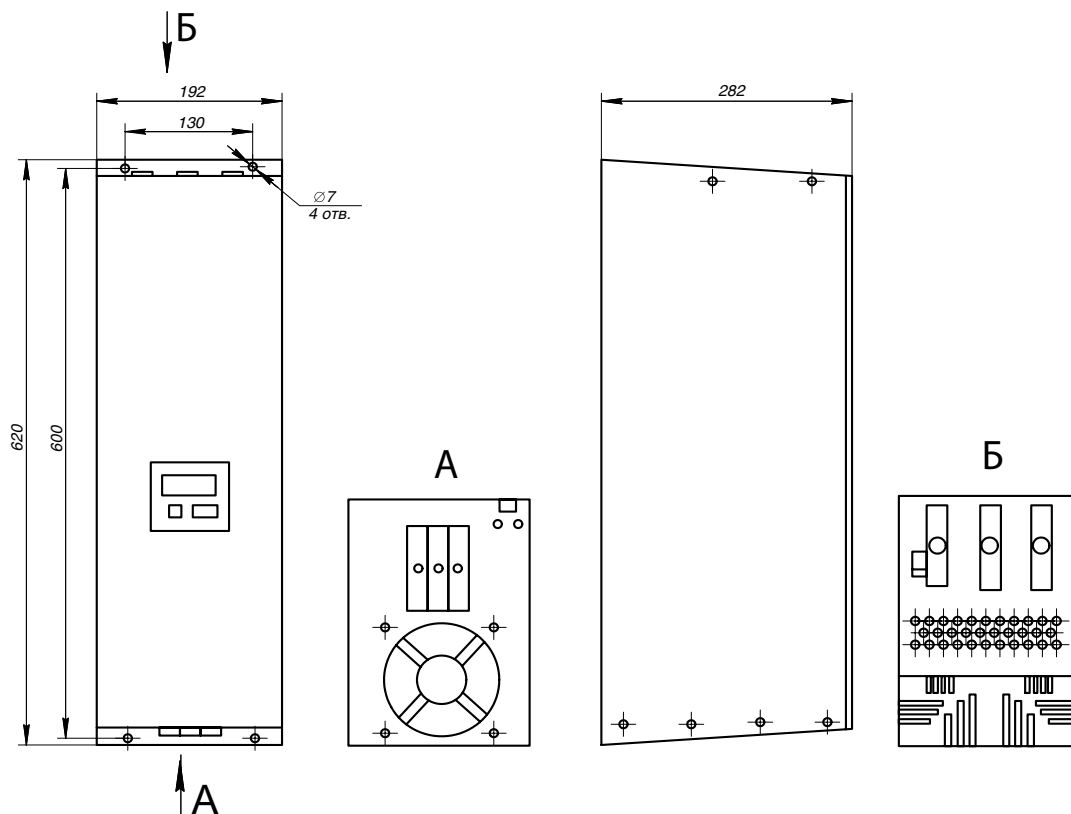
Общий вид, габаритные размеры (мм) регулятора второго типоразмера
